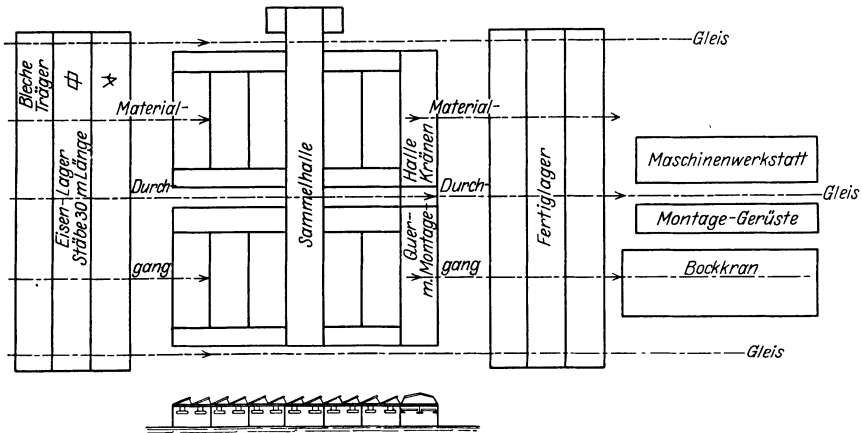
Brückenbauwerkstatt der American Bridge Co., Gary. (Nach einer Reiseskizze.)
